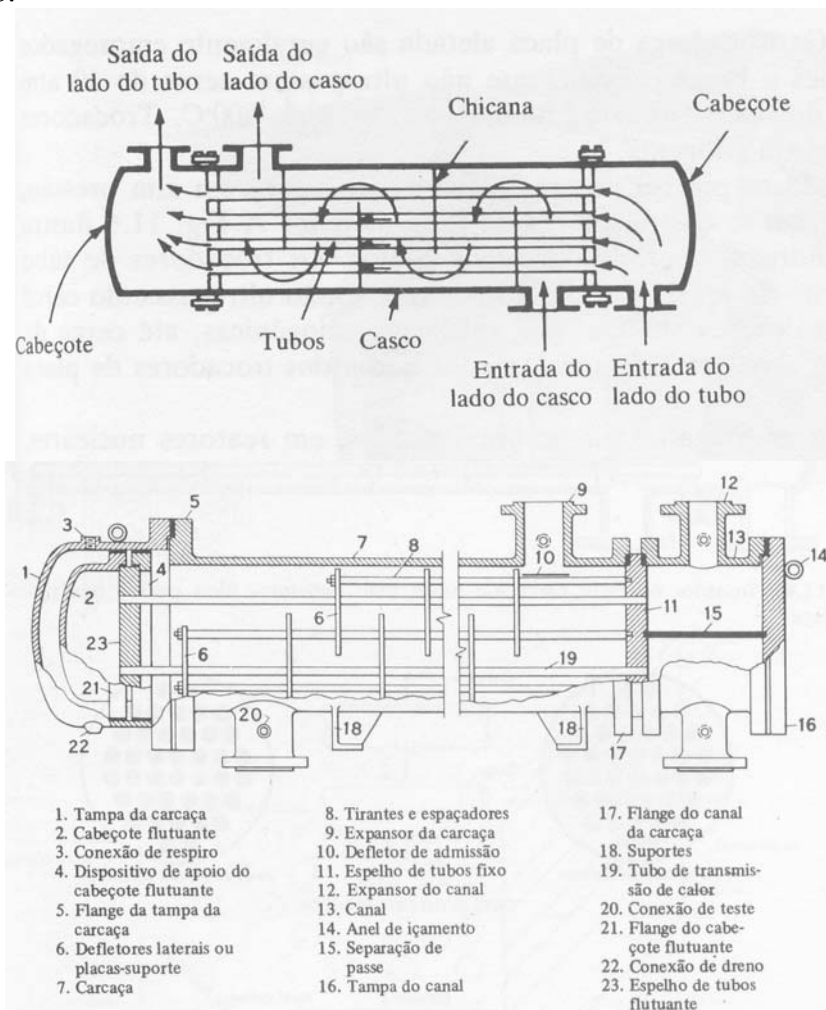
Principais partes componentes de um trocador casco e tubos.
